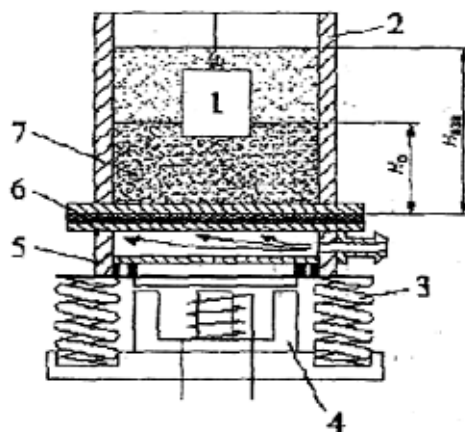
Схема вибровихревой установки: 1 - восстанавливаемая деталь; 2 - ванна; 3 - пружина; 4- вибратор; 5 - пневмокамера; 6 - пористая перегородка; 7 -
